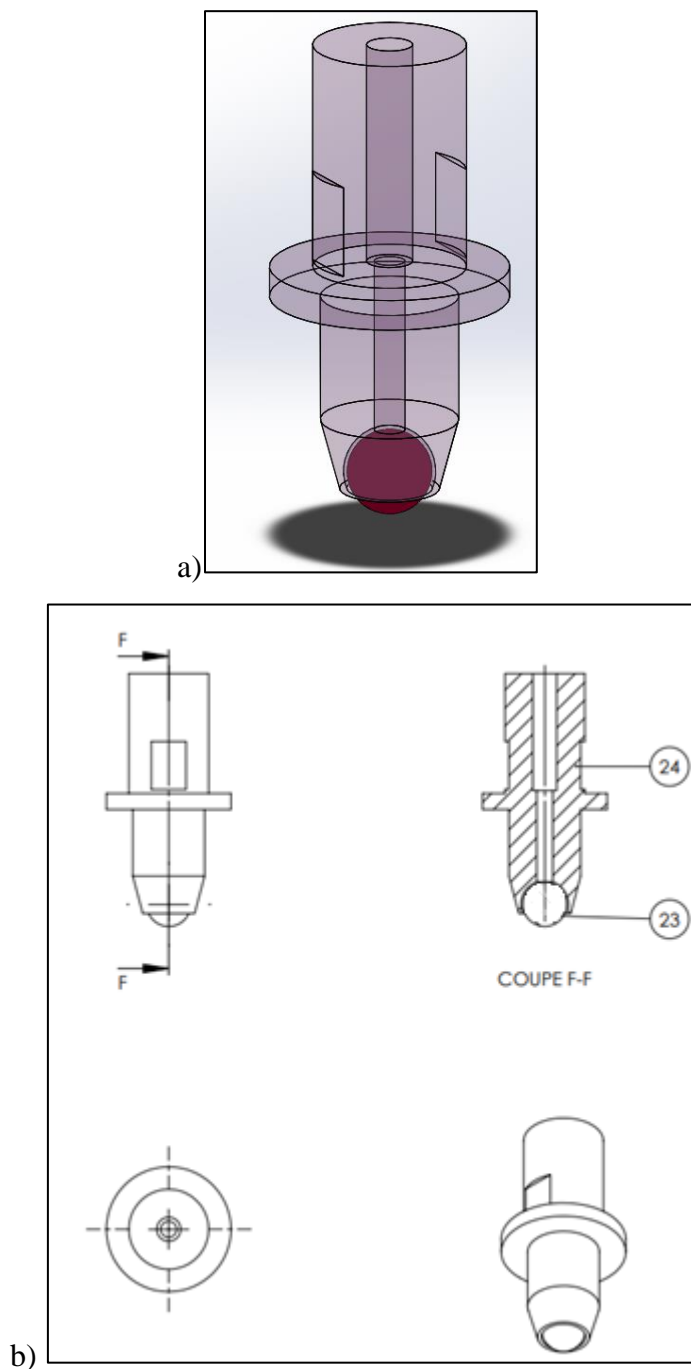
a) Vue en 3D de la tête porte bille \varnothing 6mm ; b) Dessin d'ensemble de la tête porte bille \varnothing 6mm
